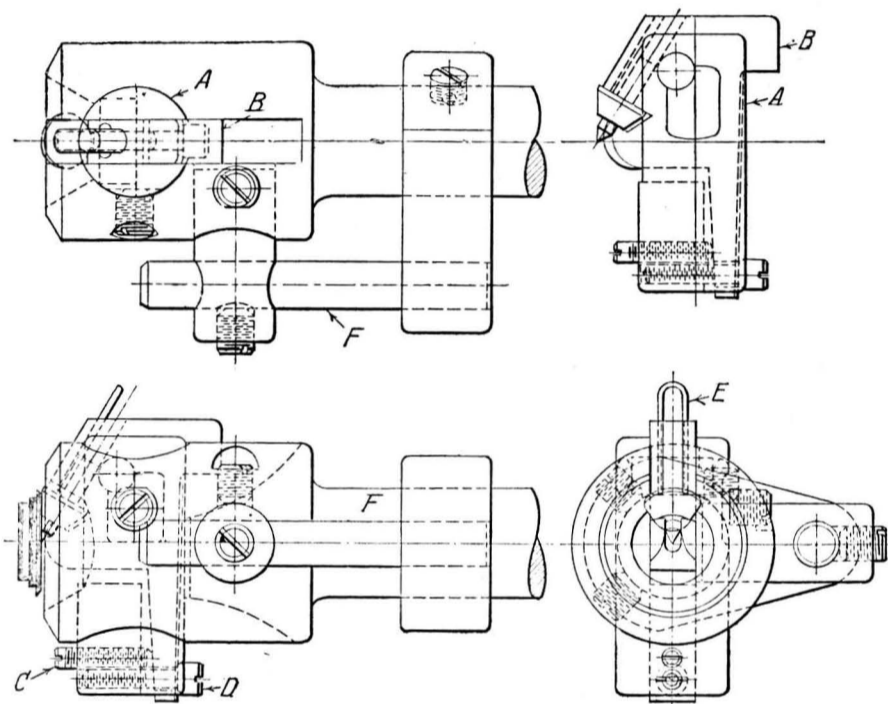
6. Kordierwerkzeug mit einer Kordierrolle.
